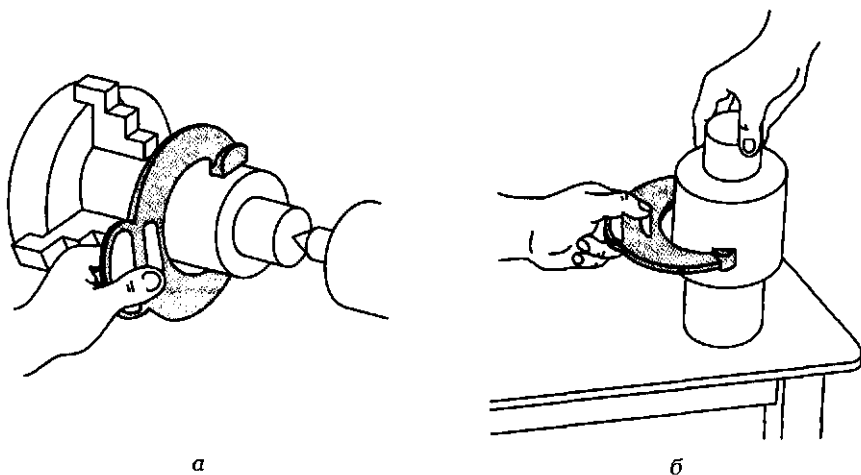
Схемы контроля деталей предельной калибр-скобой:
